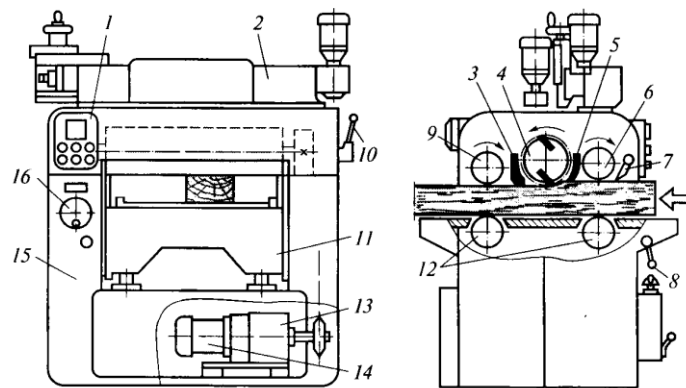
Однобічний рейсмусовий верстат: 1 – пульт керування; 2 – знімне пристосування; 3, 5 – притиски; 4 – ножовий вал; 6, 9 – вальці; 7 – кігтевий захист; 8 – рукоятка фіксування стола; 10 – рукоятка фіксатора ножового вала; 11 – стіл; 12 – опорні ролики; 13 – редуктор; 14 – електродвигун; 15 – станина; 16 – маховичок настроювання стола
